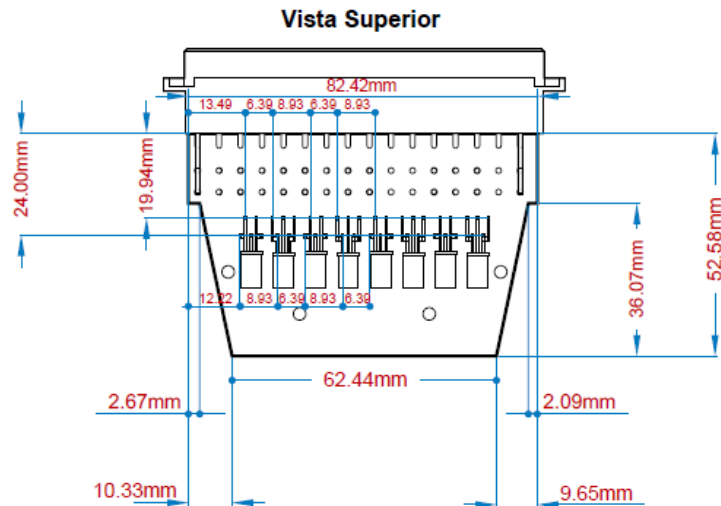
Dimensões da placa de circuito impresso da Vista superior (ver Anexo 3)
